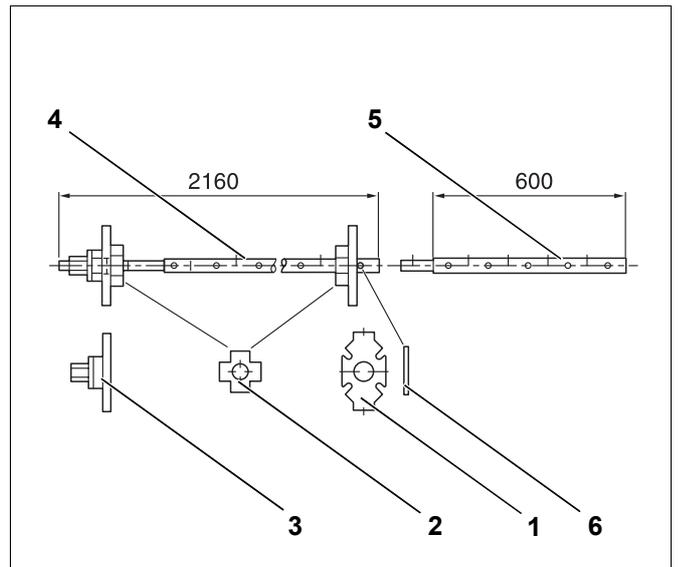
Kesselpresswerkzeug Größe 2.2 (Maße in mm)
